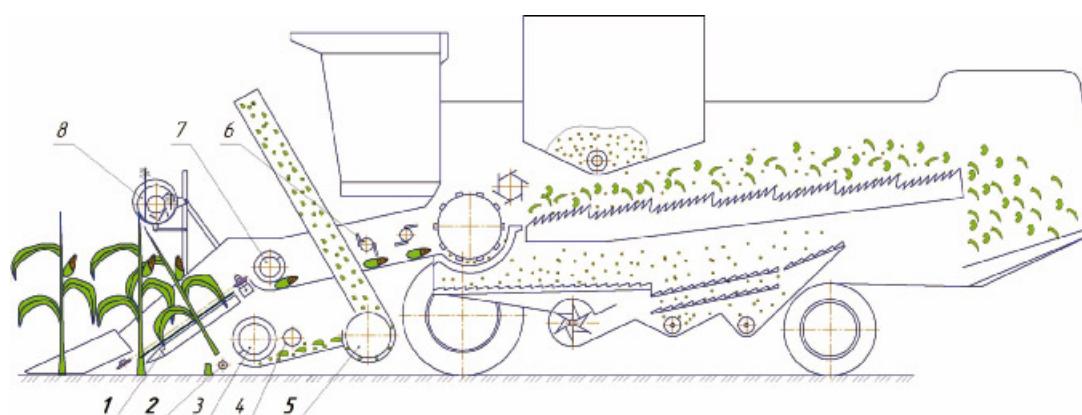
Общий вид приставки КМД-6 с дополнительным режущим аппаратом: 1 – жатка КМД-6; 2 – срезающе-измельчающий аппарат; 3 – верхний кронштейн; 4 – нижний кронштейн; 5 – ведущий шкив; 6 – кожух
